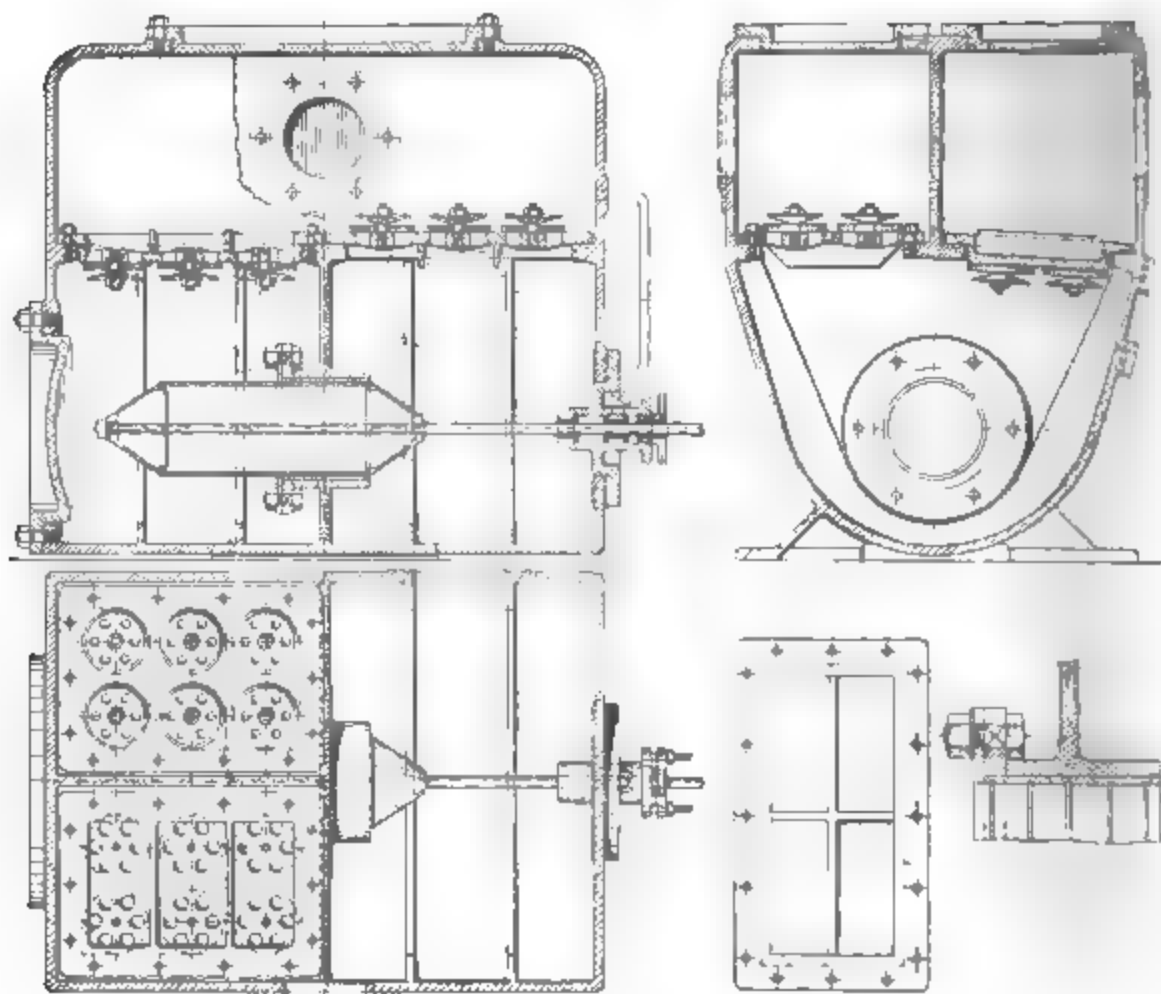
1460. Luftpumpe mit Mönchskolben.
